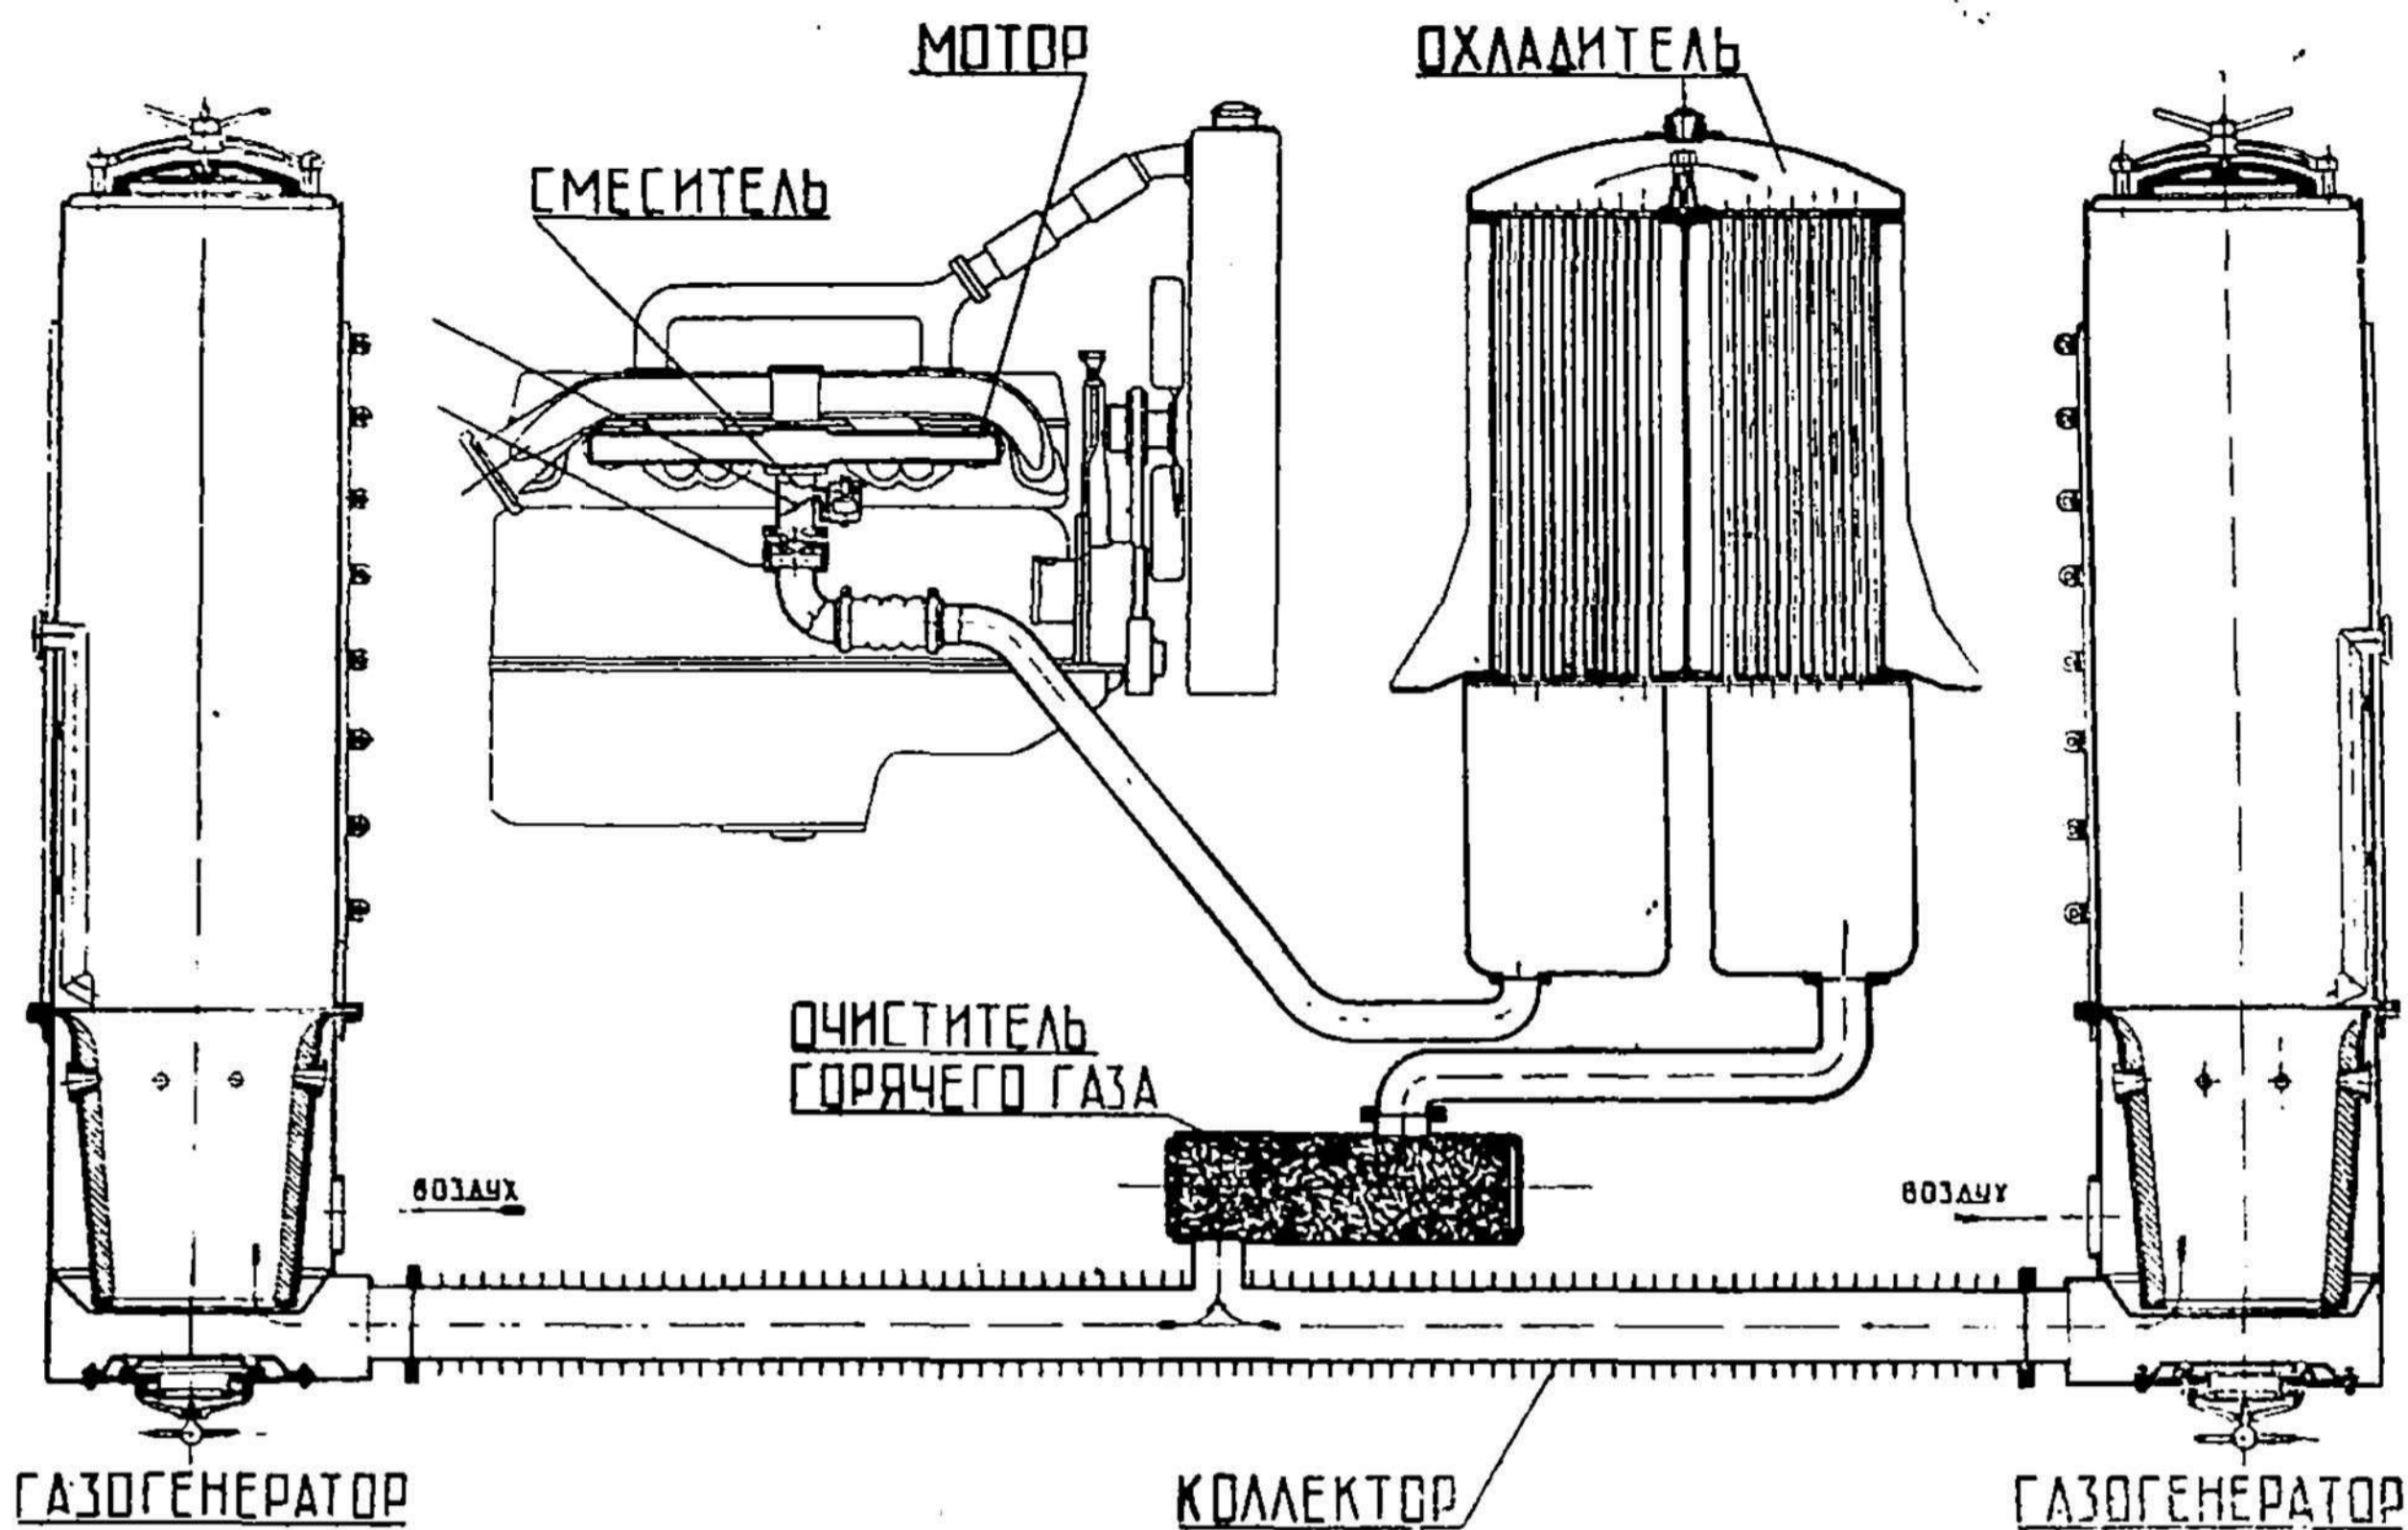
Схема газогенераторной установки конструкции В. П. Карпова для пятитонного грузовика Я-5 (пробеговой № 1).
